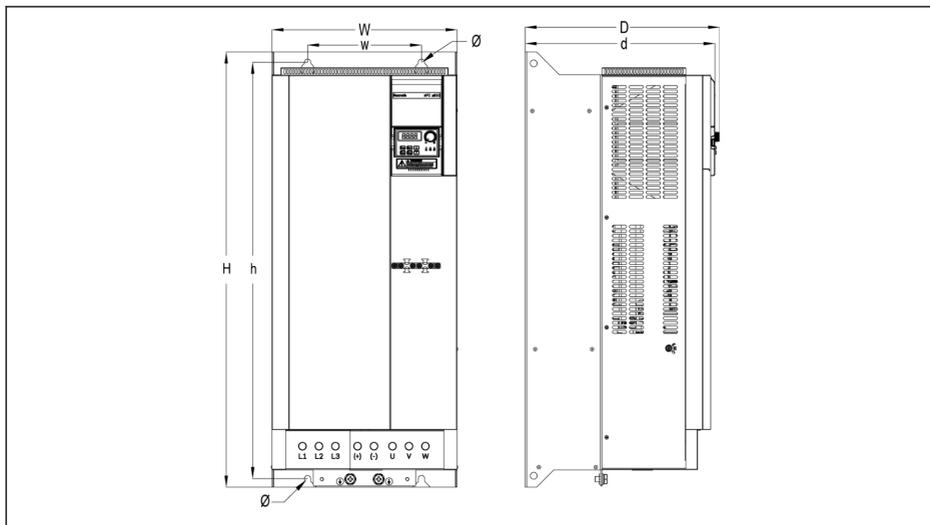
Imagen de dimensiones de EFC 5610 75K0...90K0
